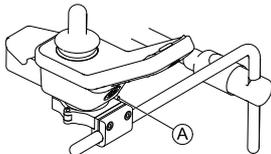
Exemple de réglage DLX-REM400. Les DLX-REM110, DLX-REM211 et DLX-REM216 sont réglés de la même manière.
